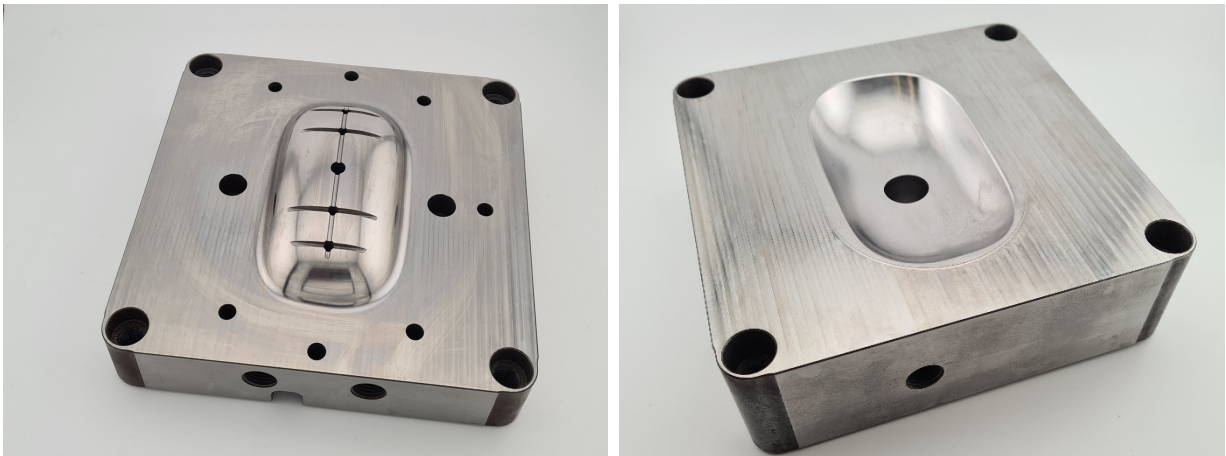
Formeinsätze mit 3d-Hybridbauteilgeometrie aus Material 1.2343 ESU gehärtet HRC 52-54
